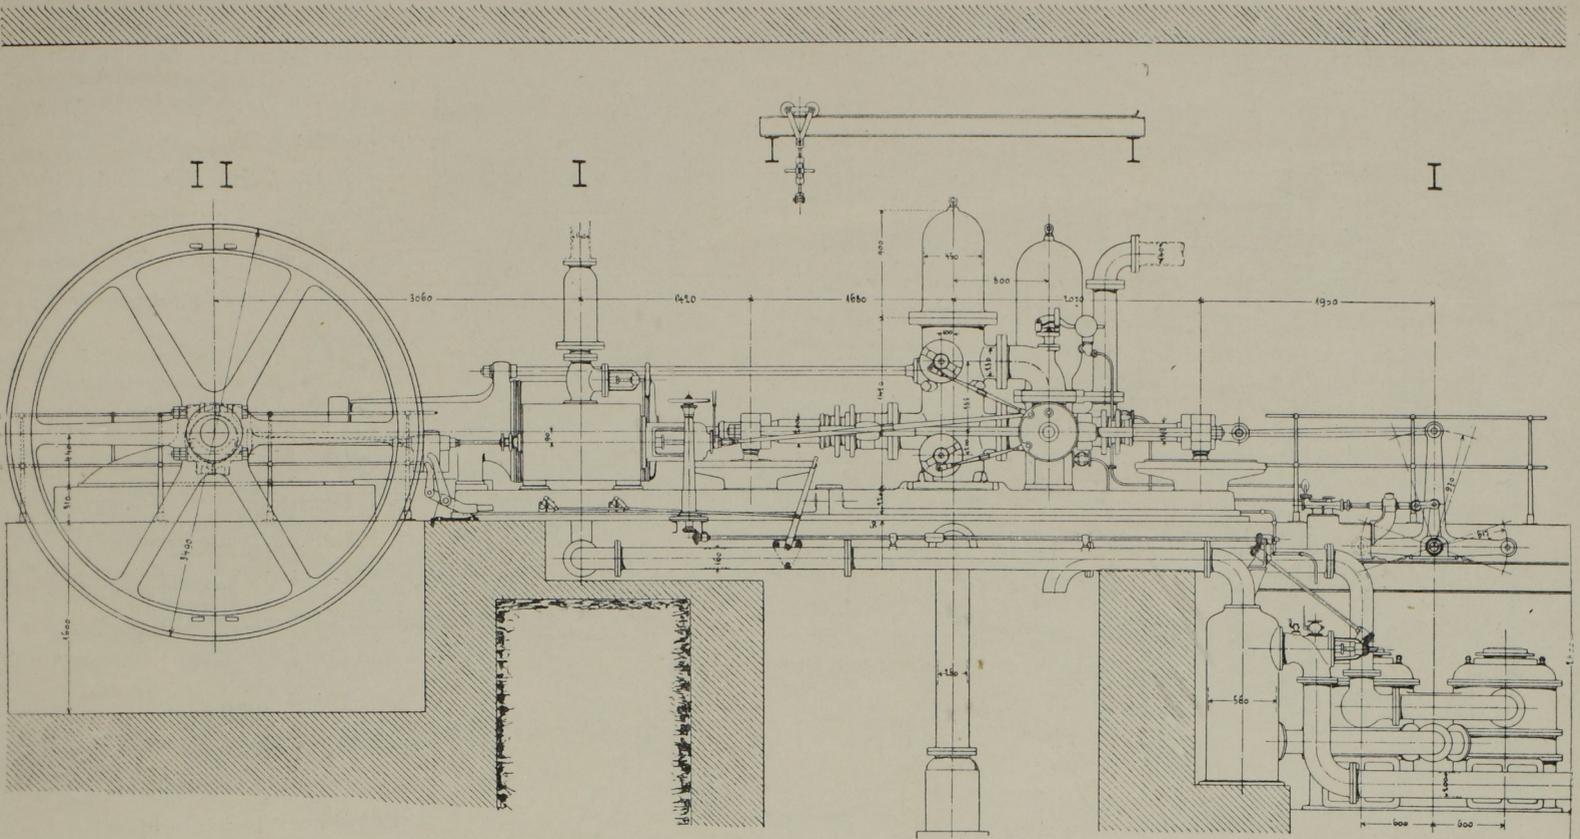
Seitenansicht der Maschine. Masst. 1:60.
